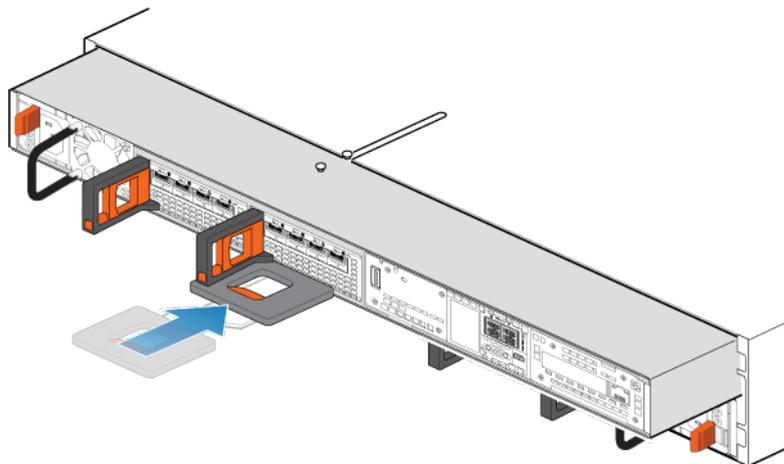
Schieben der SP-Baugruppe zur Hälfte in das Gehäuse
